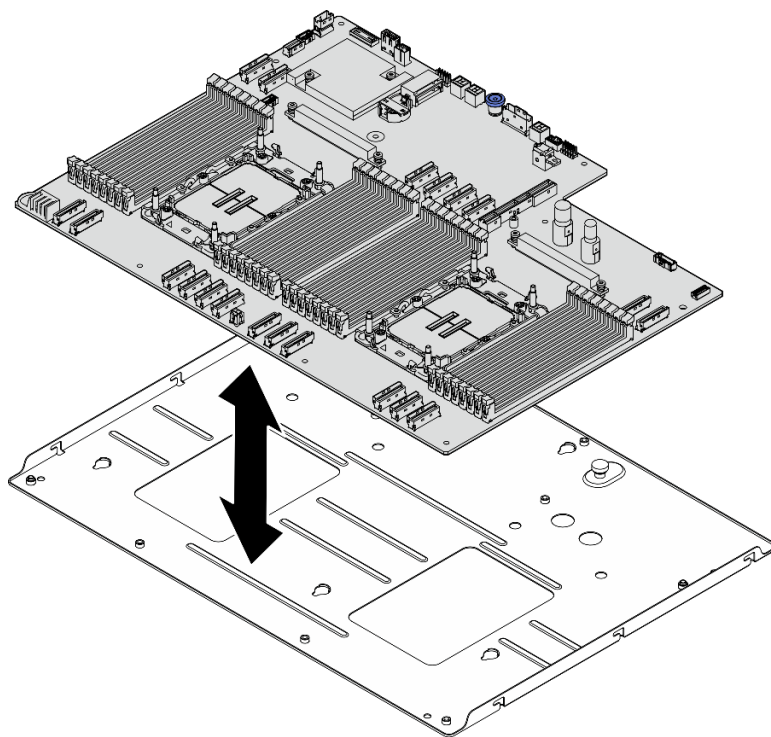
Zerlegen der Systemplatinenbaugruppe
